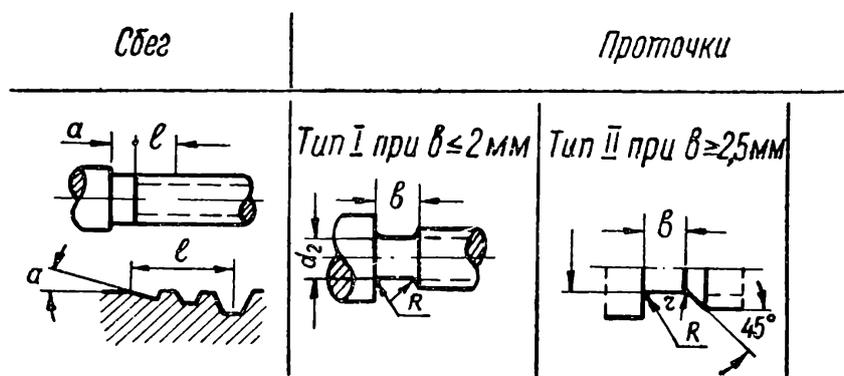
Сбеги и проточки наружной метрической резьбы.
